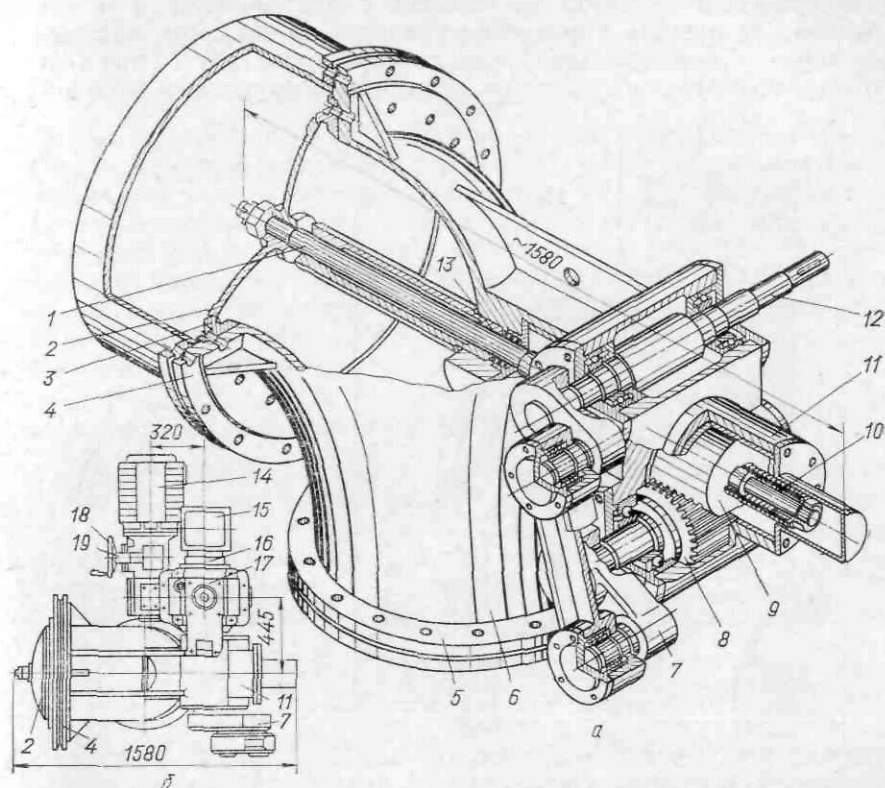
Перепускной (спускной) клапан тарельчатого типа (а) и общий вид привода (б)
